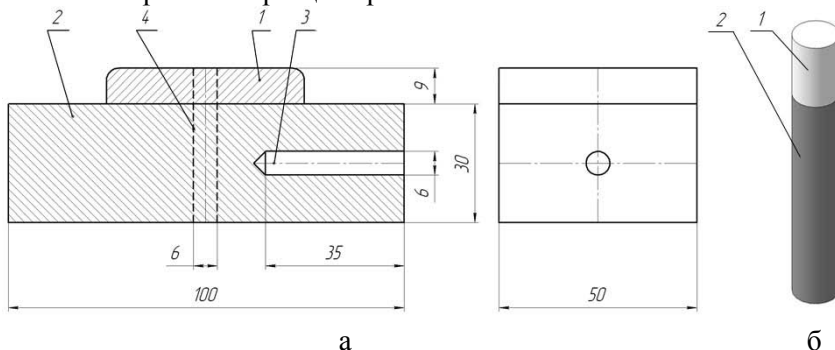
Схема подготовки образца для исследования влияния трехслойной наплавки E350T4ACG на абразивостойкость материала (а - схема заготовки для вырезания образца; б - образец для испытаний): 1 – слой, нанесенный электродуговым наплавлением; 2 – сталь 20Л; 3 – отверстие для термопары; 4 – контуры образца для испытания на изнашивание.
